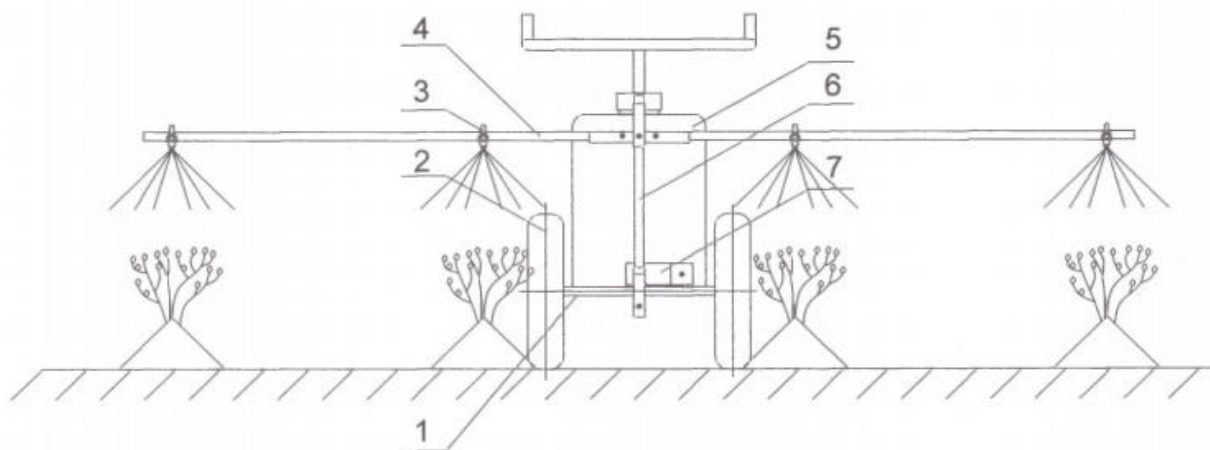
Конструктивная схема устройства для агрегата для внесения гербицидов:
